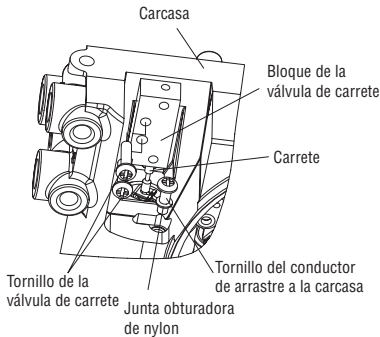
Ensamblaje de la cubierta de la válvula de carrete
